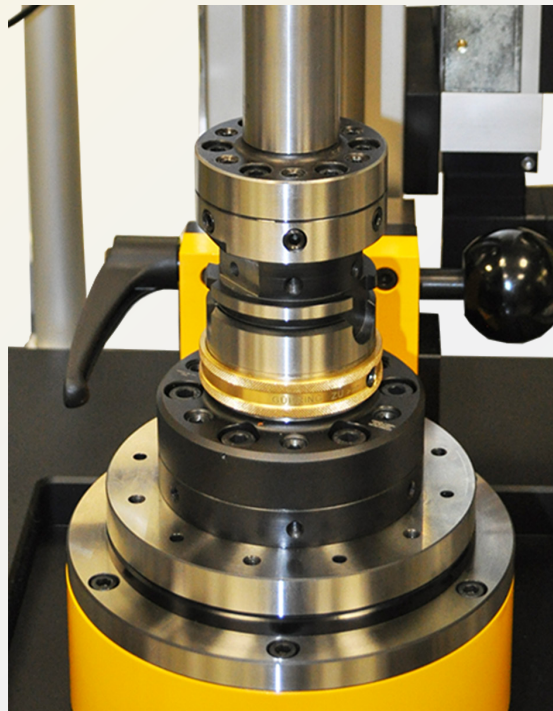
Werkzeug in HSK-Spindelaufnahme einsetzen
